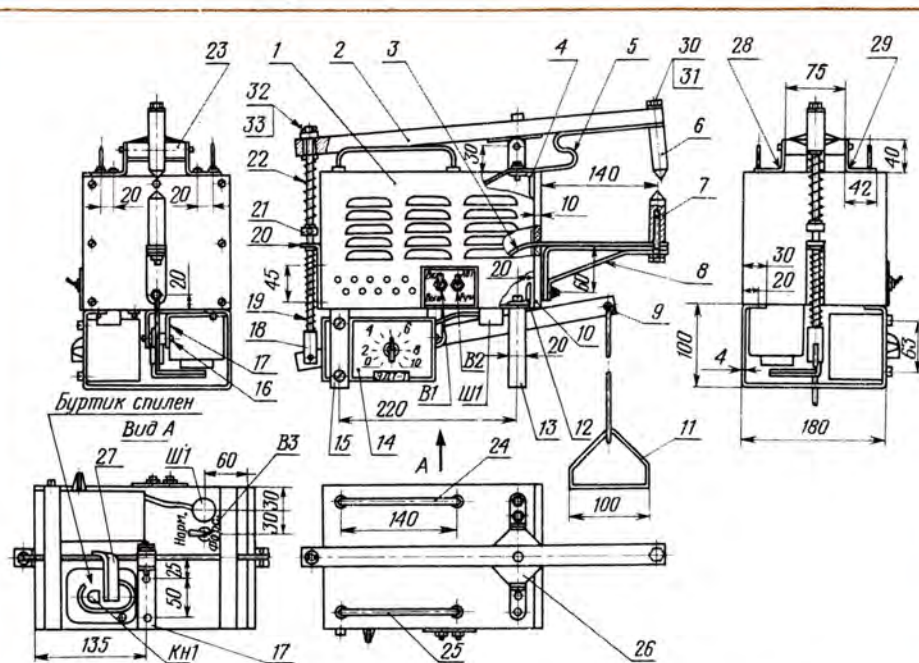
Конструкция сварочного аппарата: 1 — корпус; 2 — рычаг верхнего электрода; 3 и 5 — выводы сварочной обмотки; 4 — верхний опорный угольник; 6 и 7 — электроды; 8 — консоль нижнего электрода; 9 — педальный рычаг; 10 — опорная плита; 11 — ножная педаль; 12 — нижний опорный угольник; 13 — передняя стойка; 14 — ЭДТ; 15 — задняя стойка; 16 — ось педального рычага; 17 — подшипник оси педального рычага; 18 — толкатель рычага верхнего электрода; 19 — возвратная пружина; 20 — угольник-направитель толкателя; 21 — упор нажимной пружины; 22 — нажимная пружина; 23 — ось рычага верхнего электрода; 24 и 25 — ручки для переноски аппарата; 26 — крестовина рычага и оси верхнего электрода; 27 — угольник педального рычага; 30 — болт $M10 \times 40$ (2 шт.); 31 — пружинная шайба (2 шт.); 32 — шплинт 2×14 ; 33 — шайба (3 шт. — под шплинт, нажимную и возвратную пружины).
